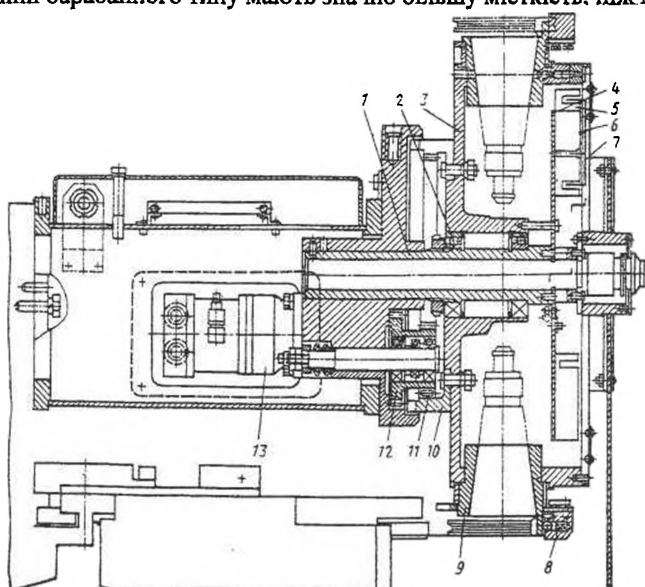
Інструментальний магазин барабанного типу:
